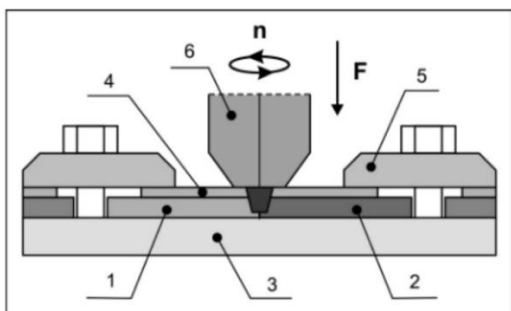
Условная схема процесса сварки трением с перемешиванием биметаллического соединения
